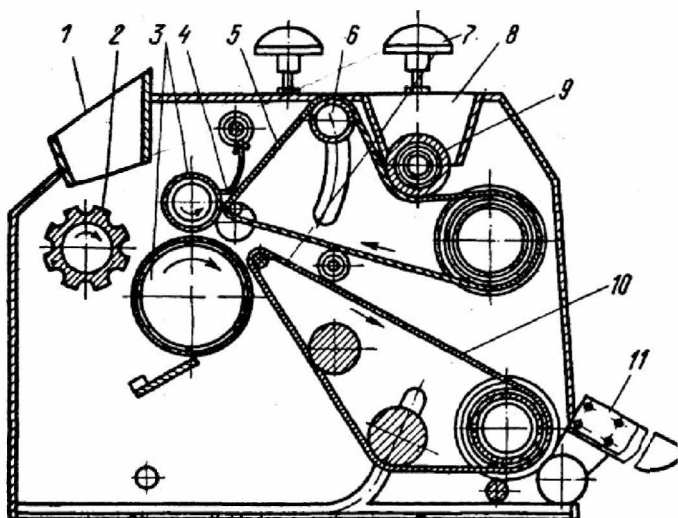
Машина для формування рогаликів С-500: 1 – приймальна лійка; 2 – рифлений валик; 3 – розкочувальні валки; 4 – ножі; 5, 10 – стрічки транспортера; 6, 7 – валки; 8 – борошнопосипач; 9 – рифлений валок.
